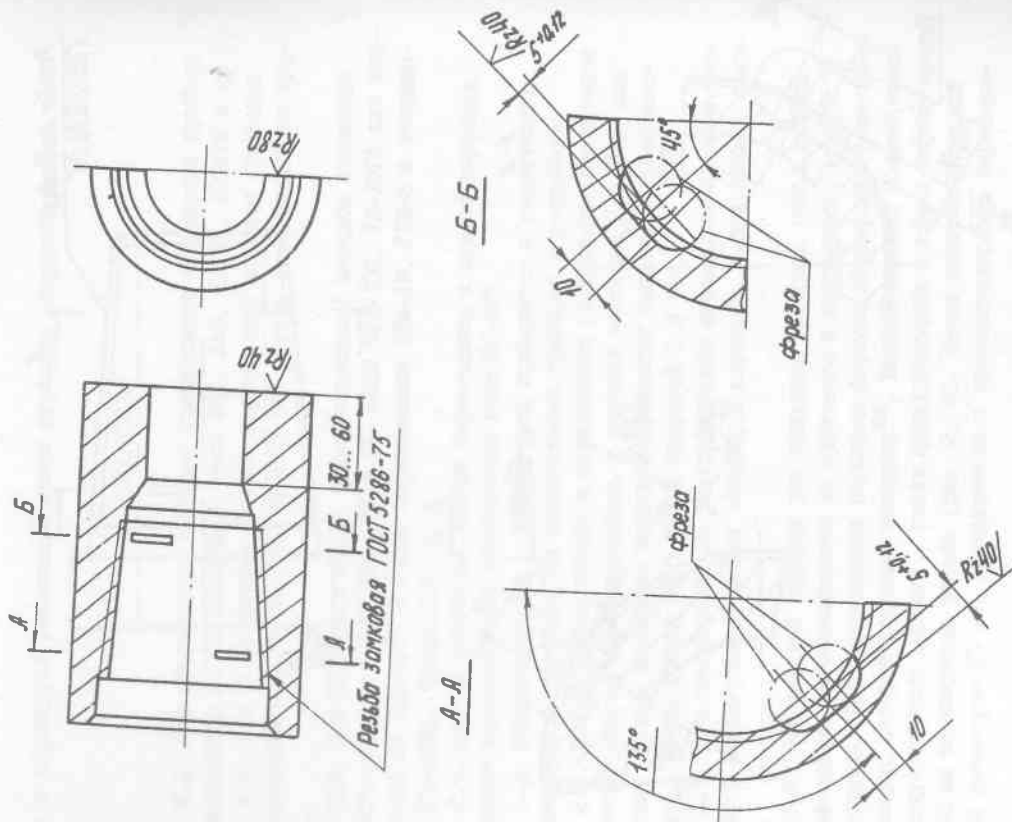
Стандартный образец для настройки ультразвукового прибора при контроле резьбы муфтового конца (сечение А-А выполнено по четвертой от торца впадине резьбы; сечение Б-Б выполнено по второй от конца сбега впадине резьбы)
